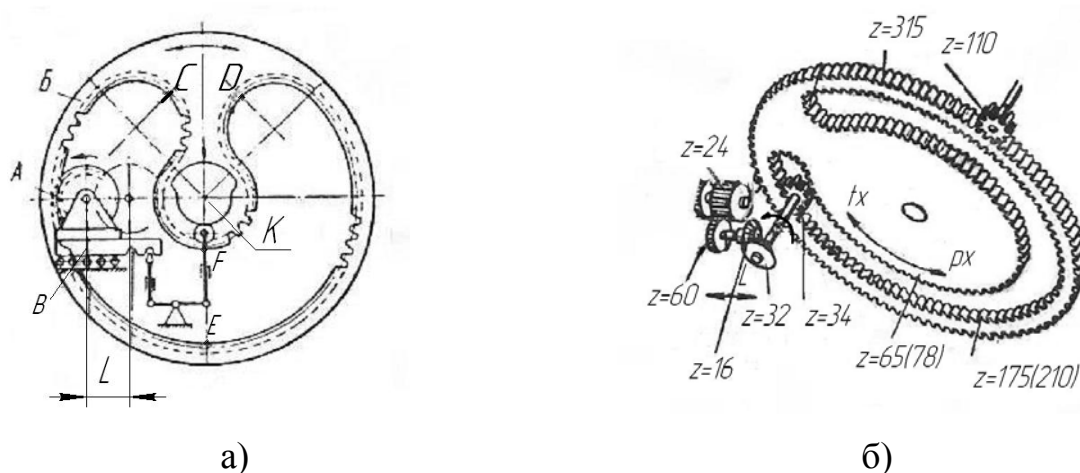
Схема реверсивного механизма: а) принципиальная; б) конструктивная
